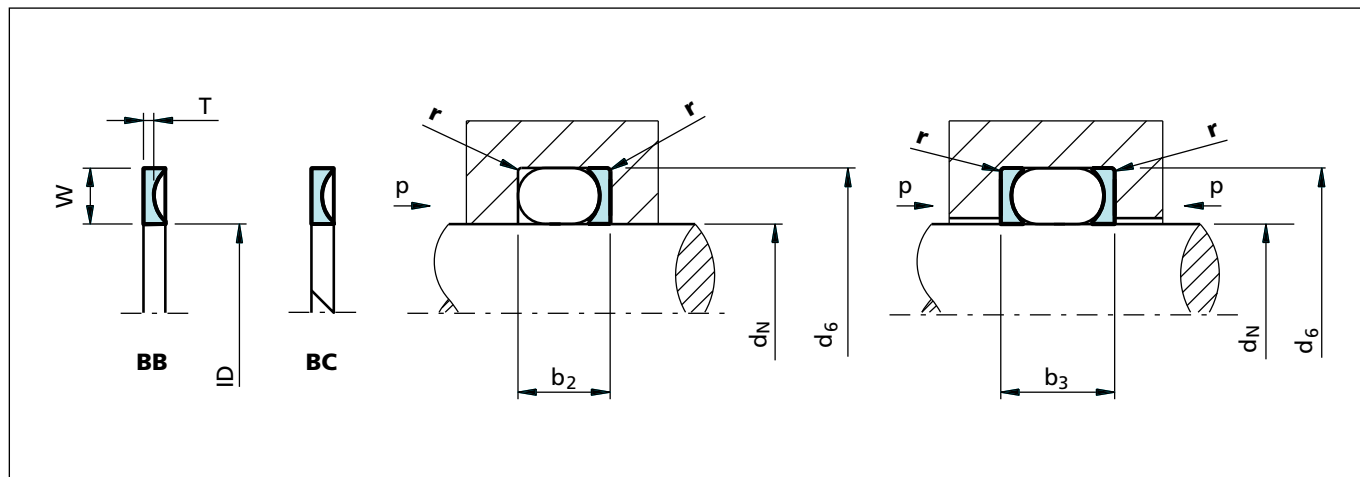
Einbauzeichnung, innendichtend, konkave Stützring Bauformen
